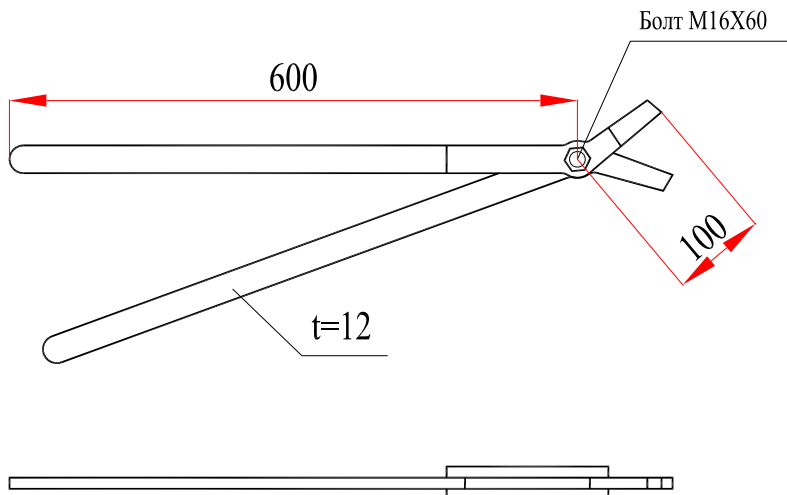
Приспособление для сборки трубы фундамента со стойкой промежуточной опоры
